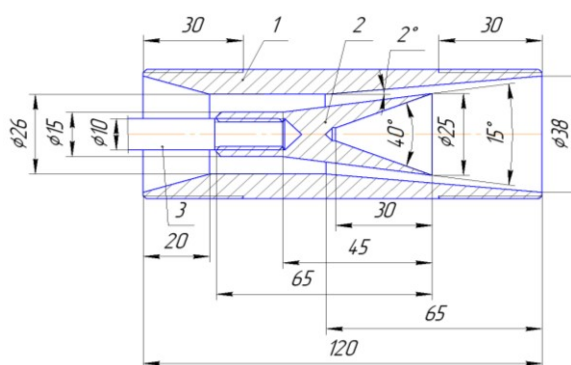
Экспериментальный образец кавитационного диспергатора: 1 – корпус; 2 – конус-обтекания; 3 – стержень
